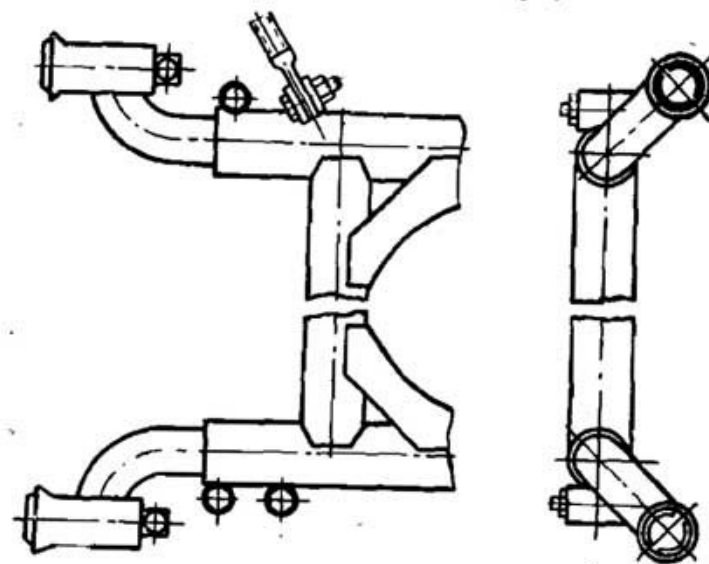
SCHEMA DE FIXATION DES SUPPORTS SUR LE CADRE DE SIDE
